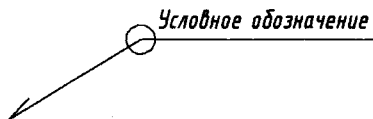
Обозначение сварного шва по замкнутой линии
